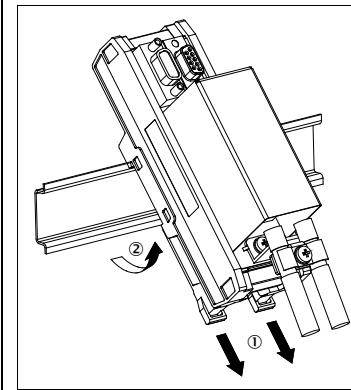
Démontage des boîtes de raccordement de codeurs
